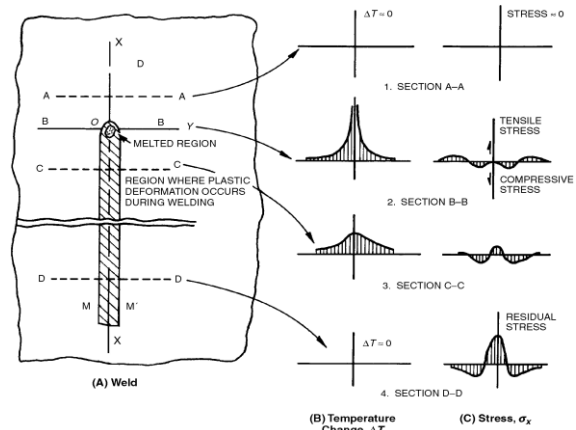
Formação de tensões residuais numa chapa soldada [3B]
